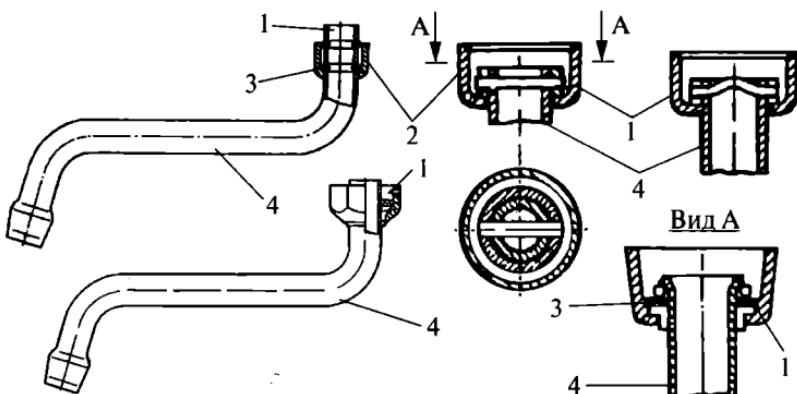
Излив смесителя пробкового типа: 1 — резиновое кольцо; 2 — накидная гайка; 3 — разжимное пластмассовое кольцо; 4 — трубка
